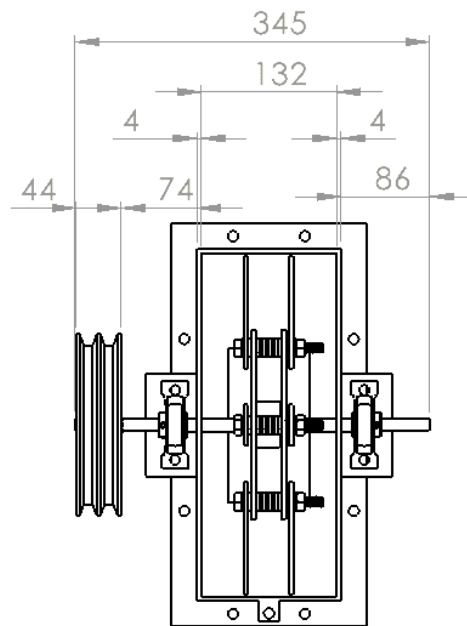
Dimensionamiento del eje (Vista de planta, cotas en mm).
